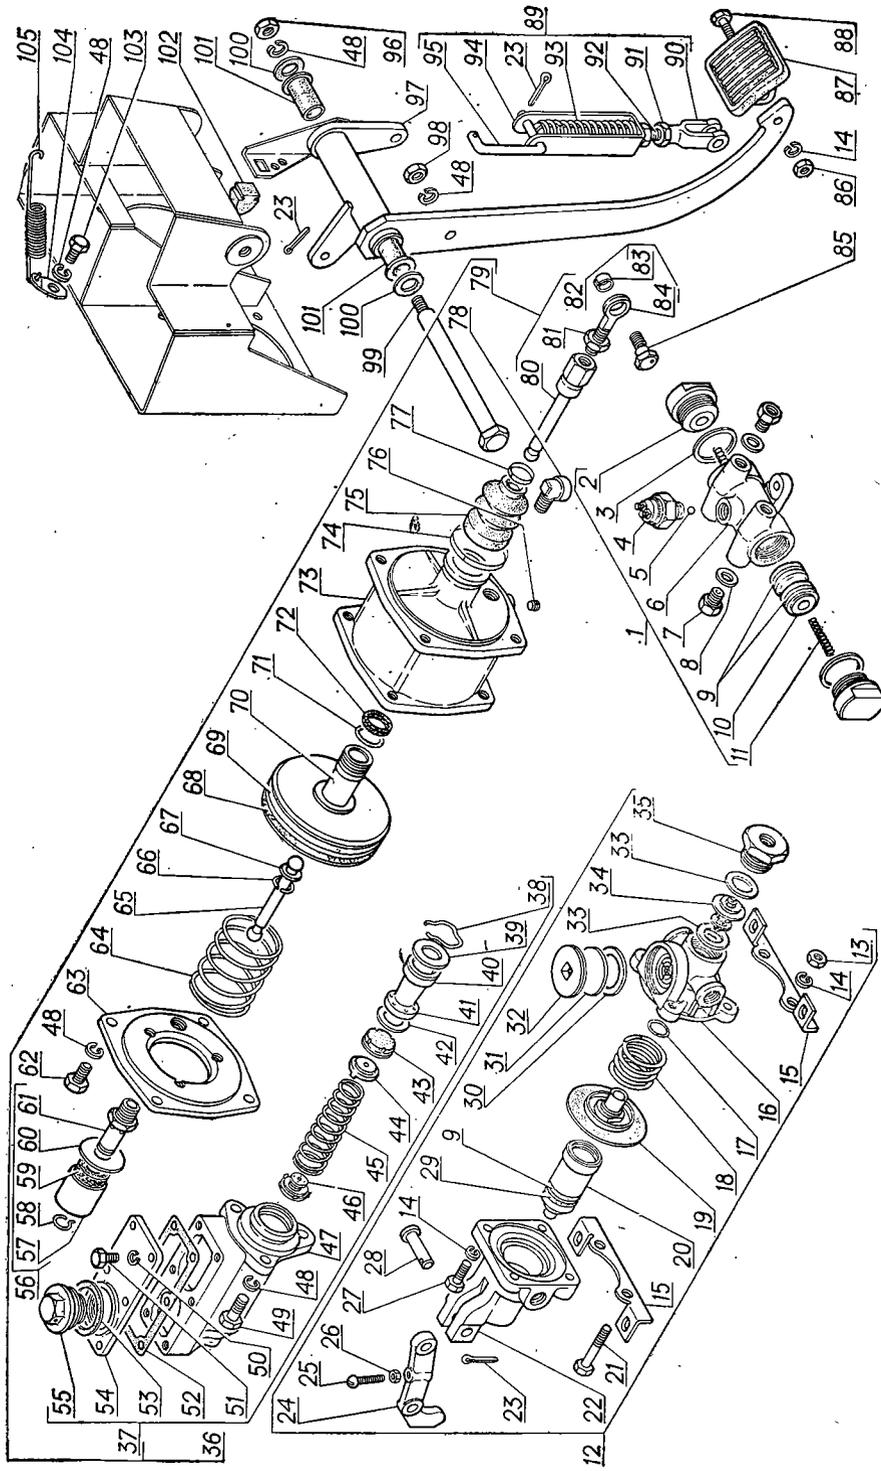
Привод рабочих тормозов, главный цилиндр тормоза, пневматический усилитель тормоза и воздушный фильтр усилителя
